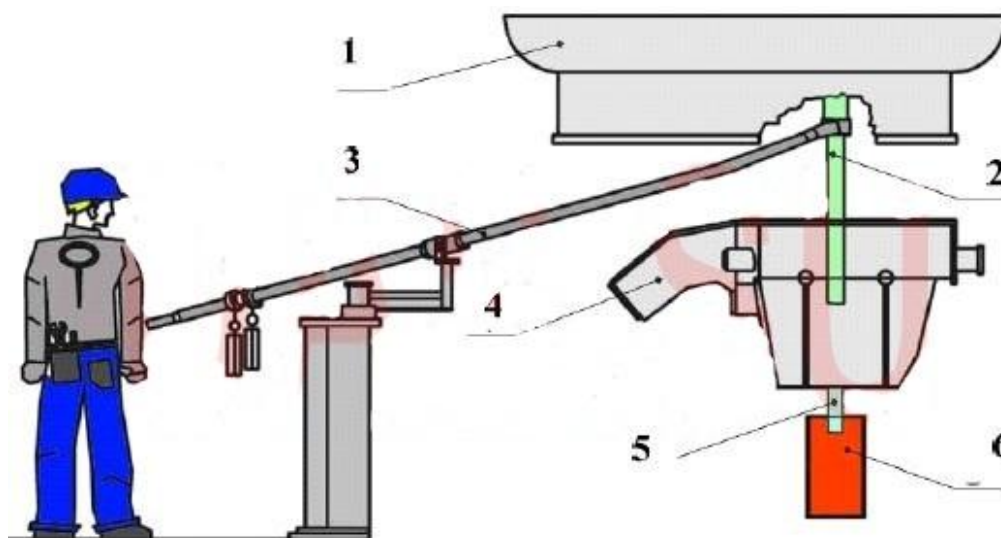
Схема перелива стали из сталеразливочного ковша в промковш закрытой струей с применением защитной трубы, устанавливаемой манипулятором: 1 – сталеразливочный ковш; 2 – защитная труба; 3 – манипулятор; 4 – промежуточный ковш; 5 – погружной стакан; 6 - кристаллизатор
